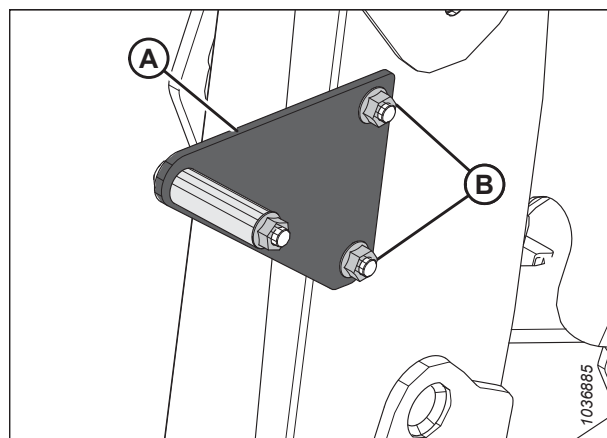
Кронштейн формовочного щитка — жатка R85
